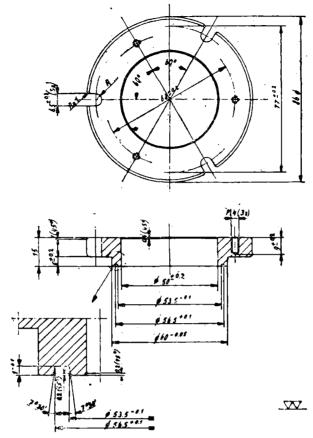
Anille de presión del recipiente (detalles en sección vertical y en planta). (Dimensiones en mm.)
